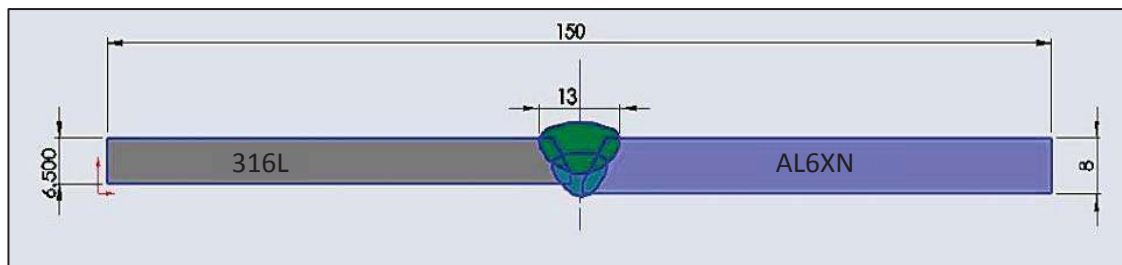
Corte transversal del arreglo de la unión soldada en 2 pasadas de soldadura, acotación en mm.
